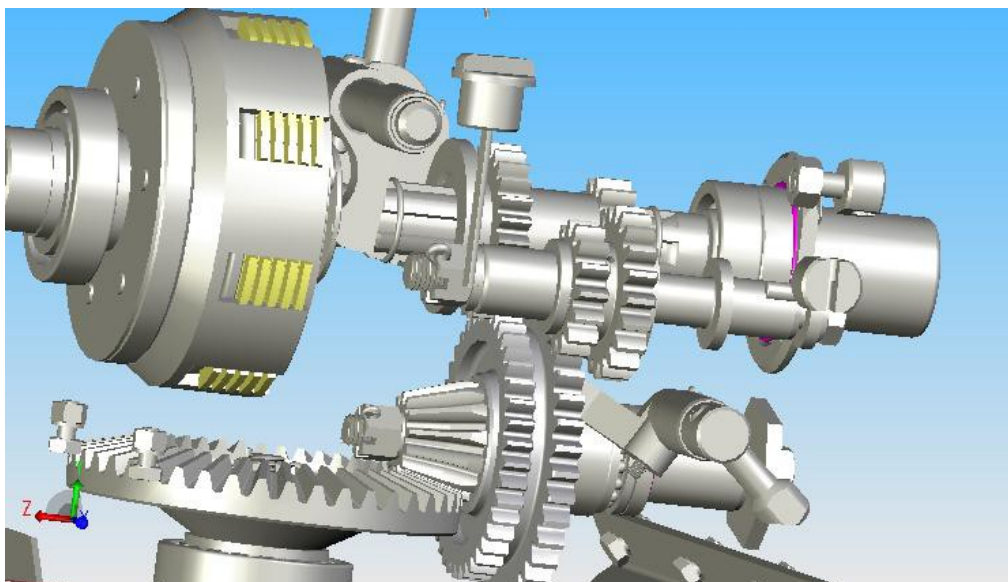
Взрывной кинематический чертёж силовой передачи мотоблока Zirka
